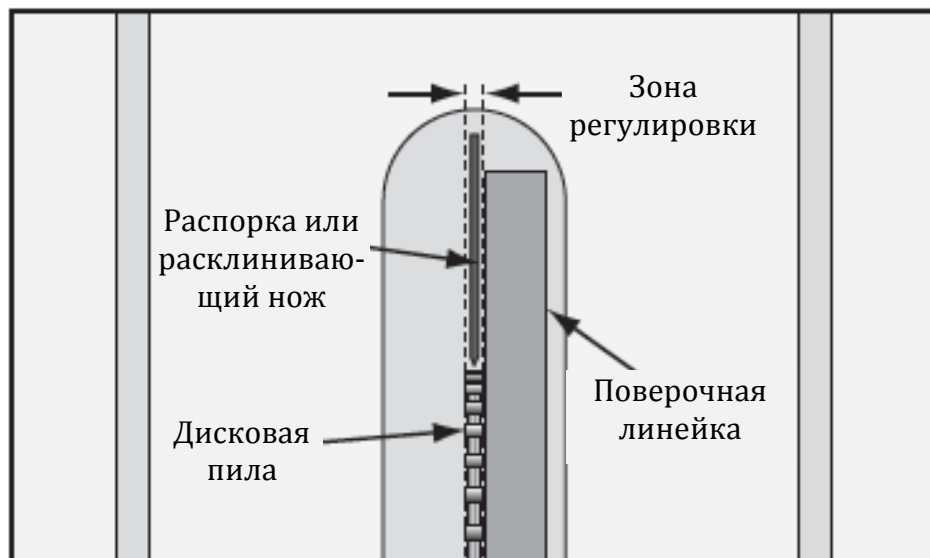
Зона регулировки распорки или расклинивающего ножа
